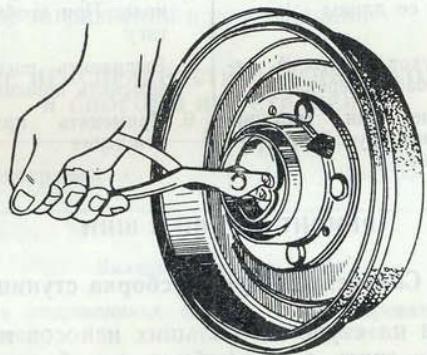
Снятие упорных колец подшипников ступицы колеса ведущего моста
